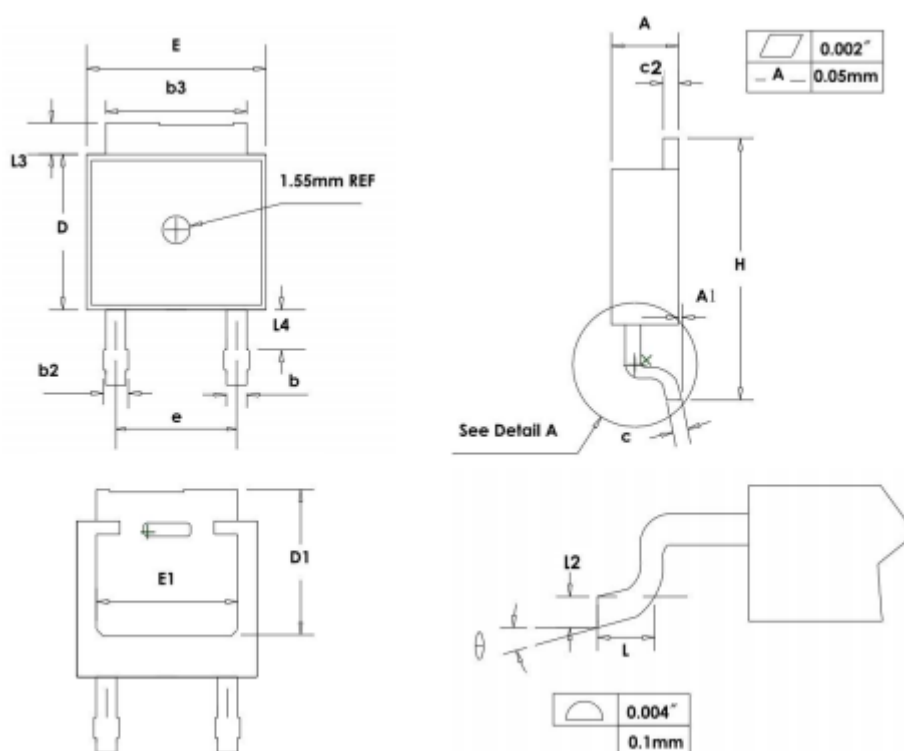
Чертеж корпуса C4D05120E (размеры в мм.)
